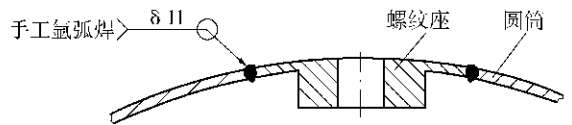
容易焊透的螺纹座与圆筒的焊接结构示意图
